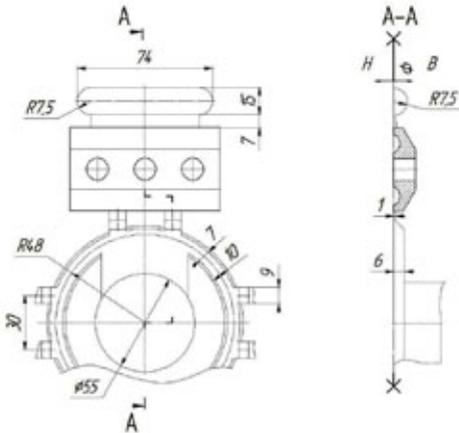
Технология изготовления отливки «Плешка» методом ЛПД
